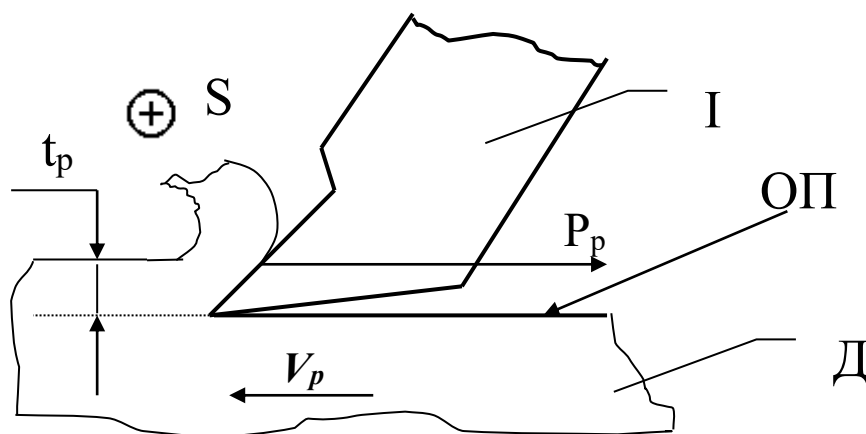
Схема різання:  $P_p$  – сила різання;  $V_p$  – швидкість різання;  $S$  – подача;  $t_p$  – глибина різання; Д – деталь; ОП – оброблена поверхня; І – різнальний інструмент.
